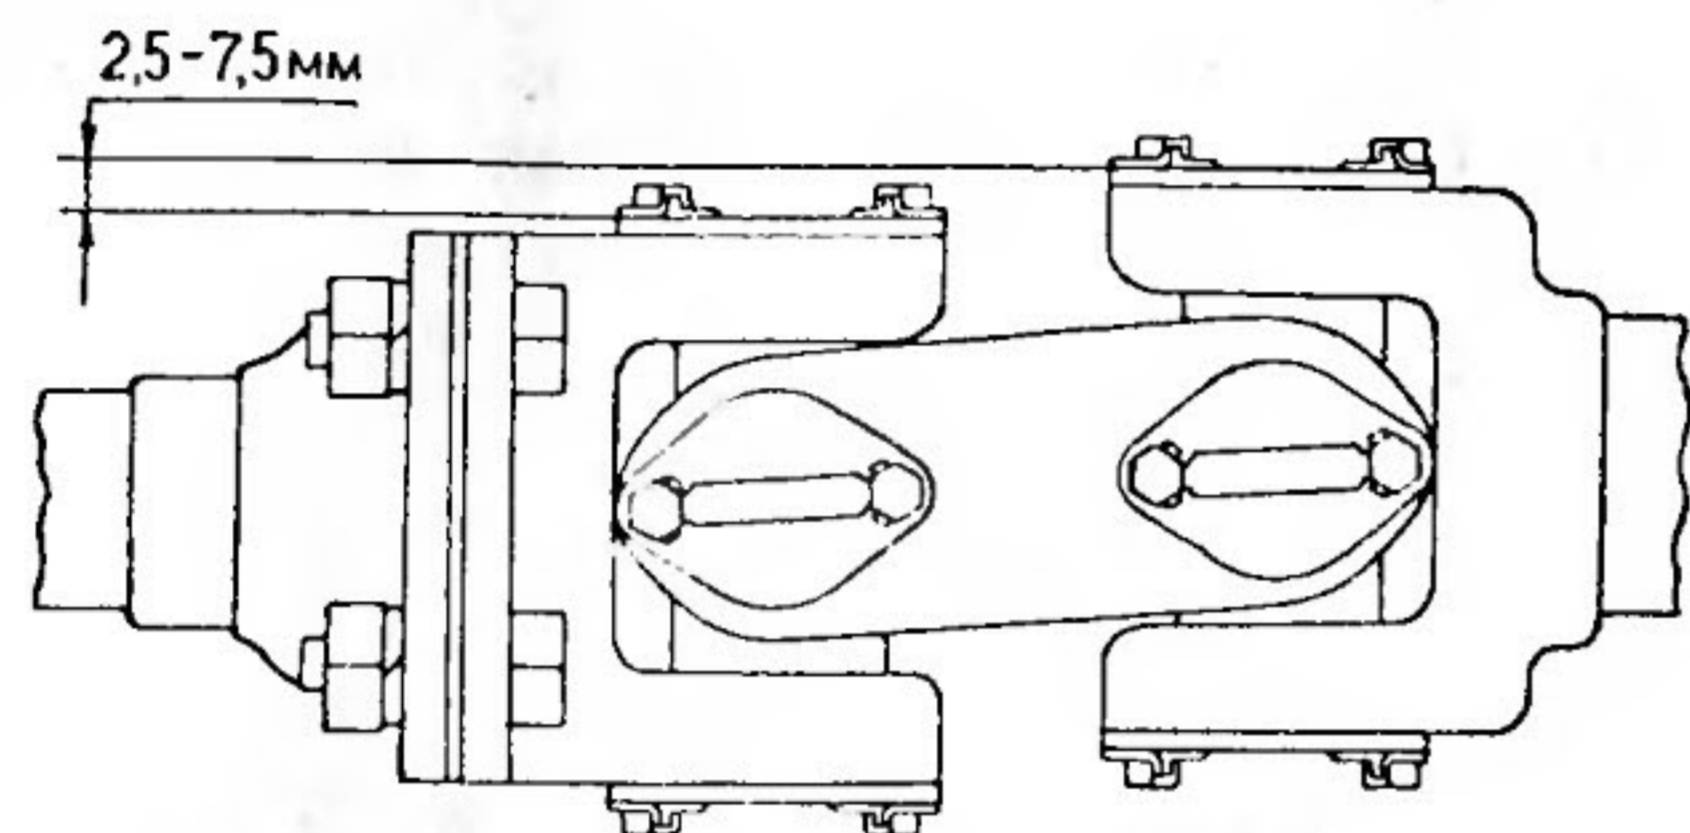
Схема проверки расположения передней и скользящей вилок карданного вала
